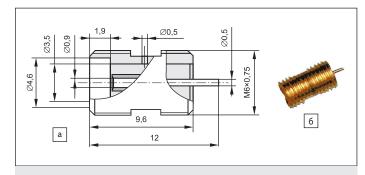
Соединитель ТС2.236.072-01: а) конструкция; б) внешний вид
